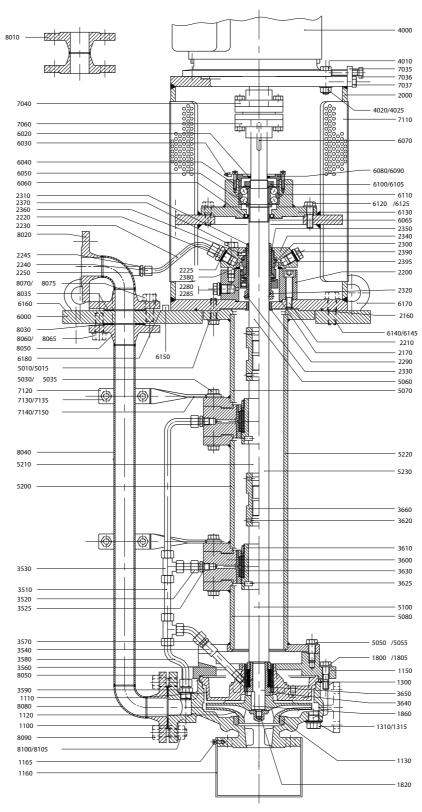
Pompe avec groupe d'étanchéité d'arbre M2.
